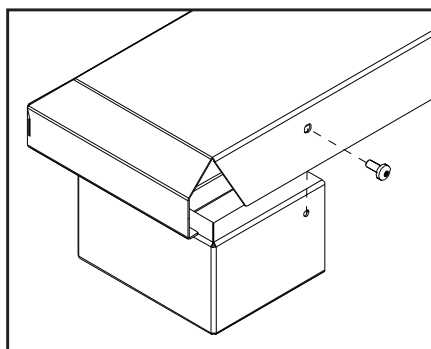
Installation de l'étagère de base sur la colonne montante.
